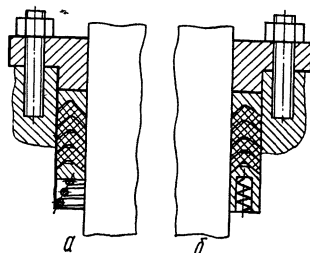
Конструкция уплотнительного узла с прижатием шевронных манжет: а — одной пружиной; б — несколькими
